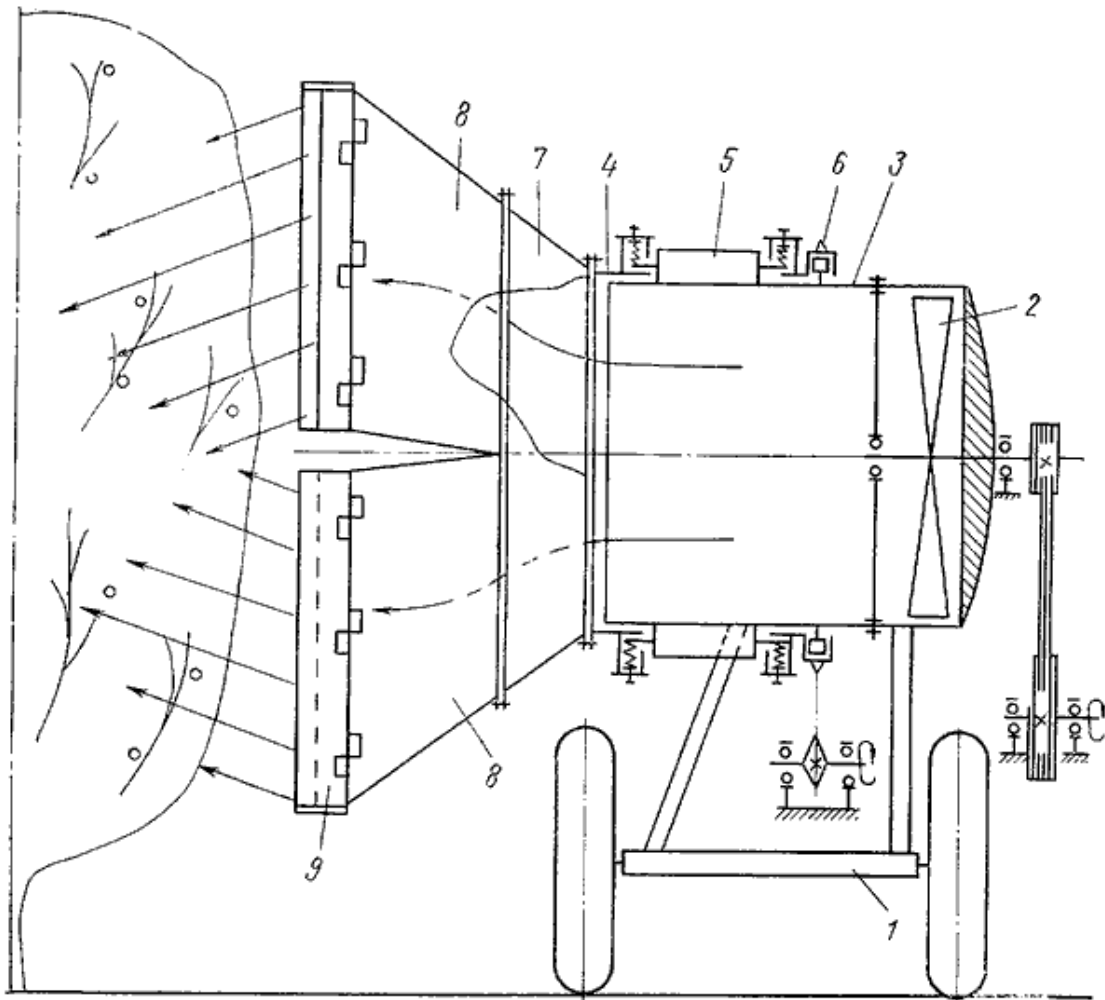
Загальний вигляд пневмострушувача для дерев.
